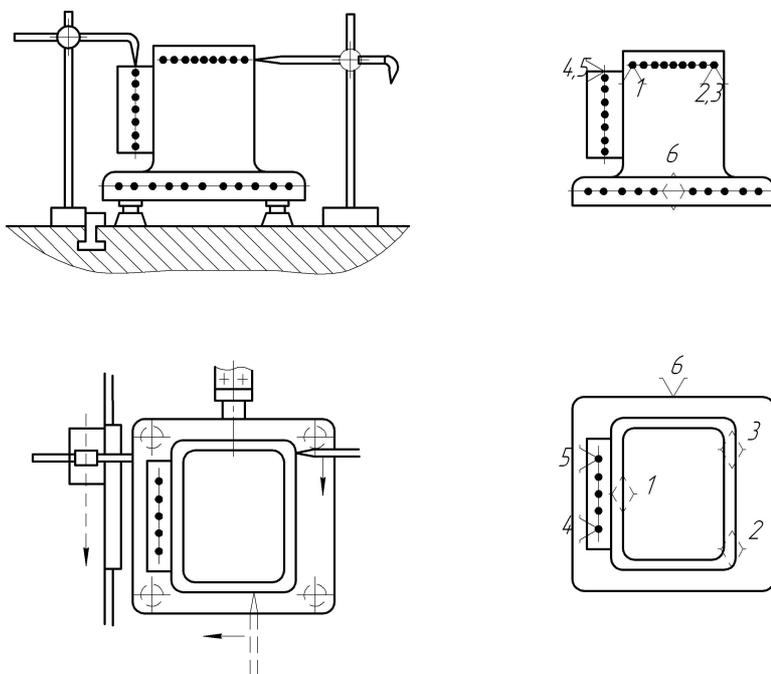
Установка на станке заготовки корпусной детали с выверкой ее положения по разметочным рискам: 1 – 6 – опорные точки
